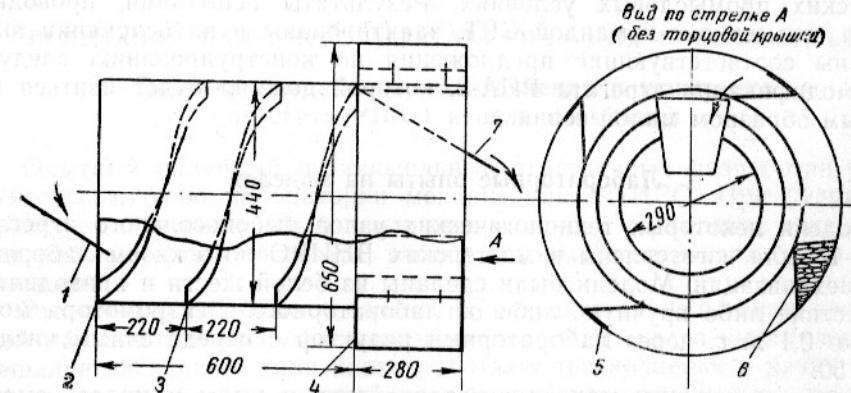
Схема модели цилиндрического смесителя с внутренней винтовой направляющей и выгрузочным устройством:
